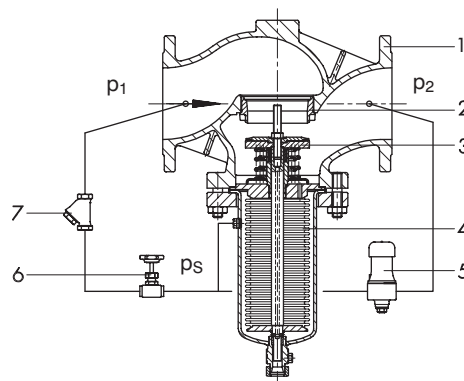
· Редуктор давления тип 2333 (Ду 125 до Ду 500), Принцип работы
